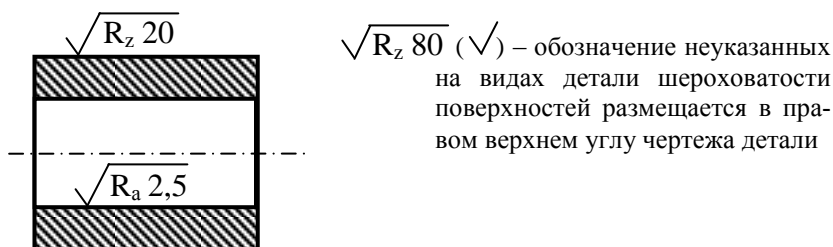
Обозначение шероховатостей поверхностей
